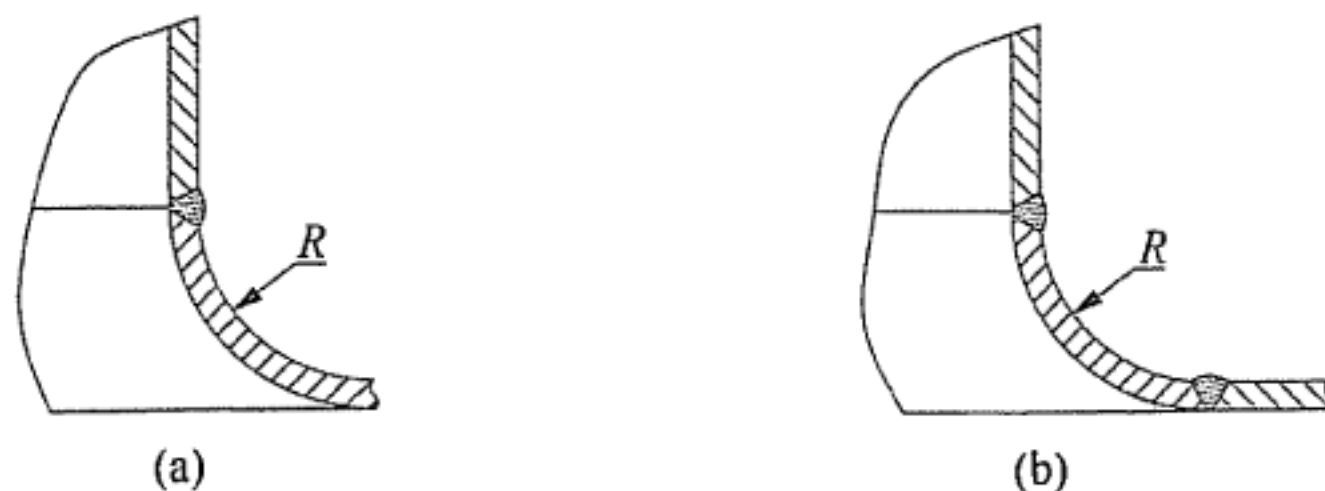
易吸收焊接变形的焊接结构示意图
